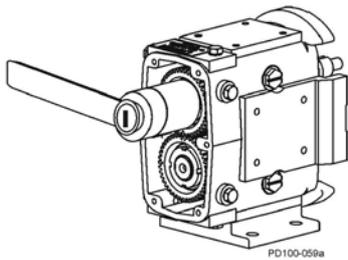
Einbau Zahnrad-Befestigungsmuttern
